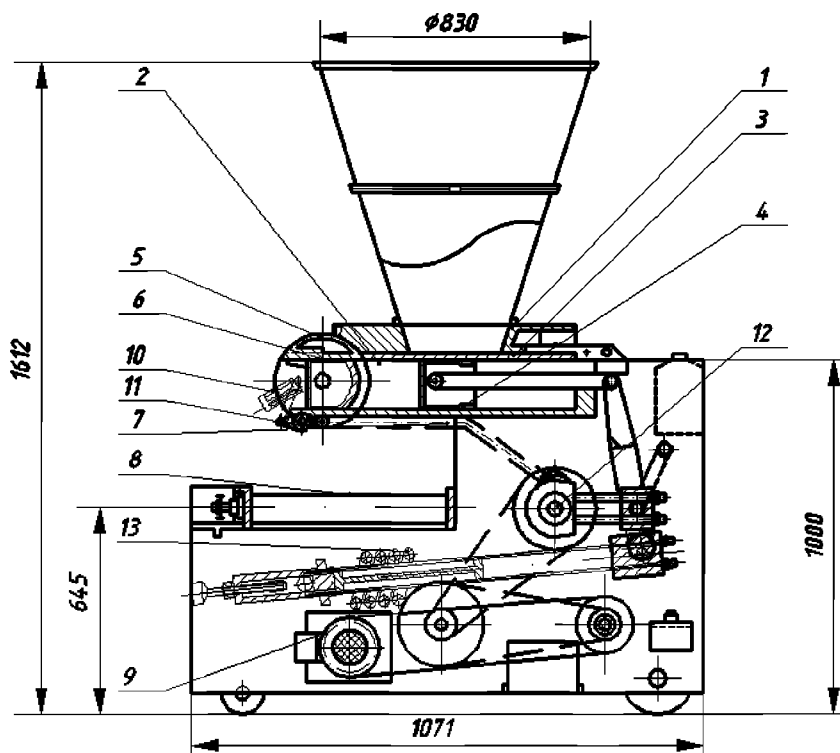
Тістоподільна машина Parta: 1 - воронка бункера; 2 - всмоктувальна камера; 3 - ніж; 4 – нагнітальний поршень; 5-заслінка тістоподільної головки; 6 - мірний поршень; 7 - важіль подільної головки; 8 - транспортер; 9 – привід; 10 - регулятор маси; 11 - виштовхувачі тістових заготовок; 12 - колінчатий вал; 13 - пружинний демпфер.
